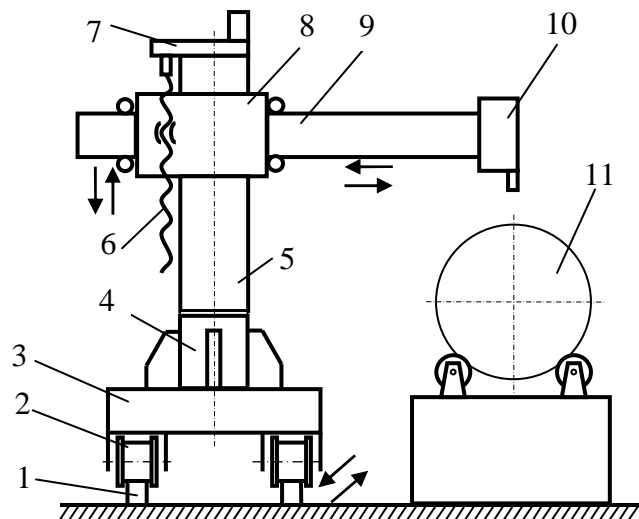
Глагольний візок: 1 – рейка; 2 – каток; 3 – платформа; 4 – основа; 5 – стояк; 6 – гвинт ходовий; 7 – редуктор; 8 – каретка; 9 – штанга висувна; 10 – зварювальний апарат; 11 – виріб.
